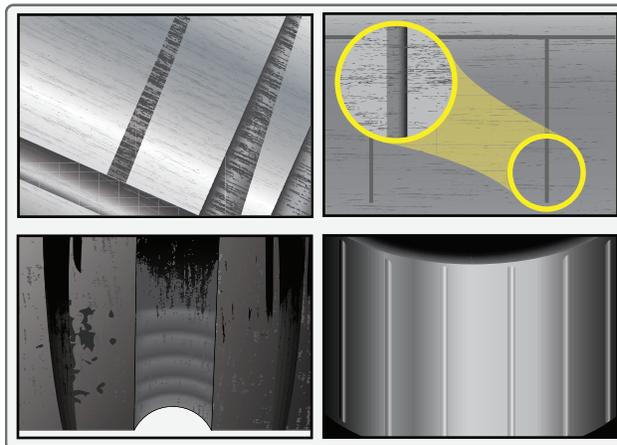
O efeito Brinell é causado por um impacto excessivo. Parece com recortes nas pistas do rolamento. Qualquer sobrecarga estática ou forte impacto pode causar o verdadeiro efeito Brinell, o que conduz à vibração e falha prematura do rolamento.
